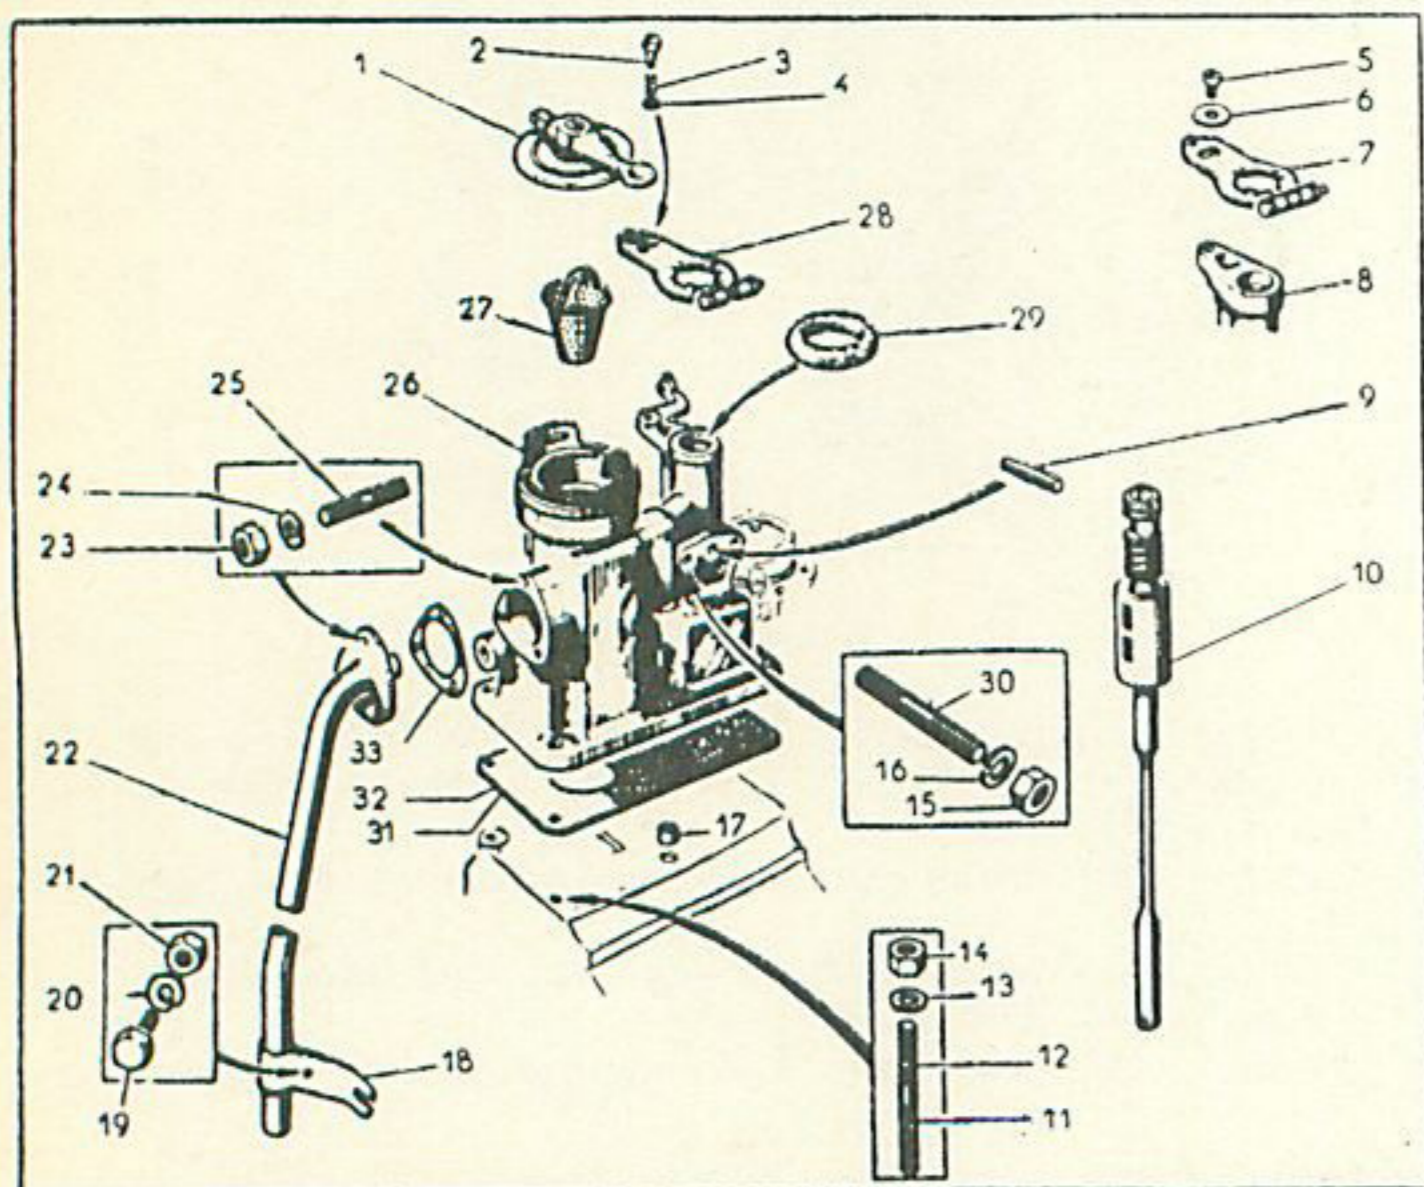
Ensemble dépresseur, couvercle et reniflard.
